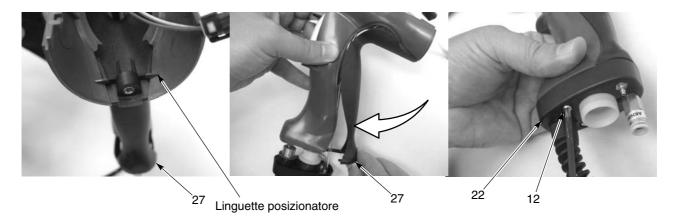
Montaggio della piattina di terra e della base alle impugnature
